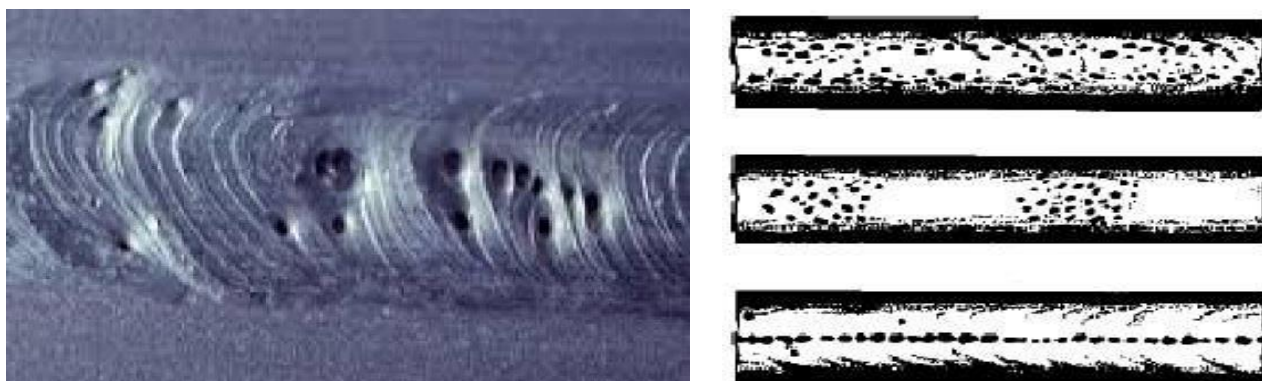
Поры и шлаковые включения в сварном шве
